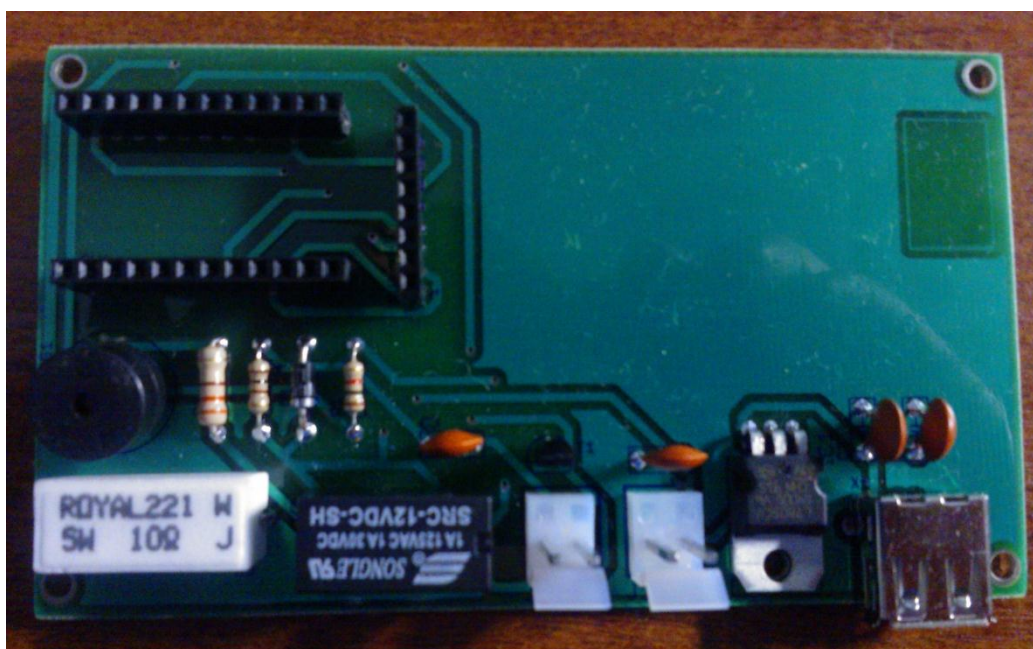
PCB IMPLEMENTADO A DOBLE CAPA. FUENTE: EL AUTOR
